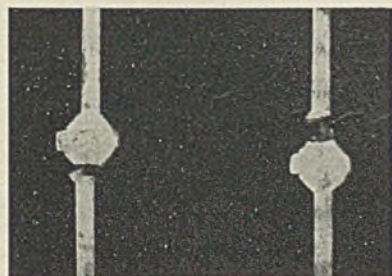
Dauerbrüche an elektrisch geschweißten Kreuzstoßproben.
